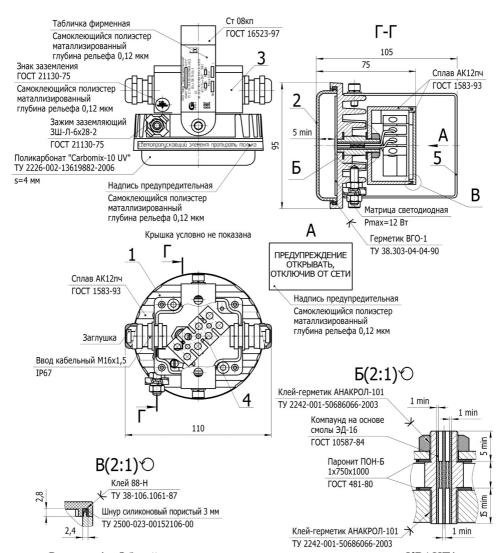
Общий вид и чертеж взрывозащиты светильников КВАНТ1 (1 – Корпус; 2 – Светопропускающий элемент; 3 – Отделение вводов; 4 – Клемма; 5 – Скоба; 6 – Труба)
